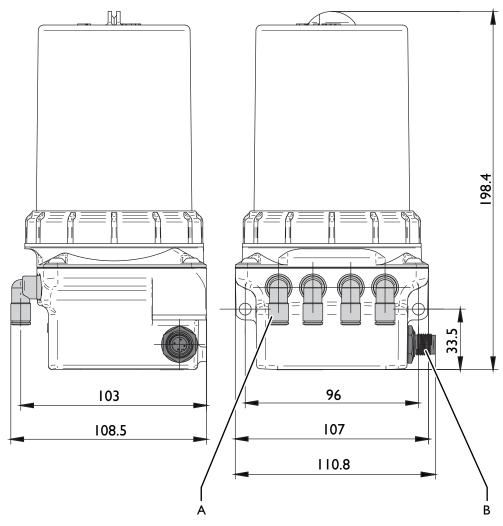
Dimensioni e collegamenti FlexxPump4 D
